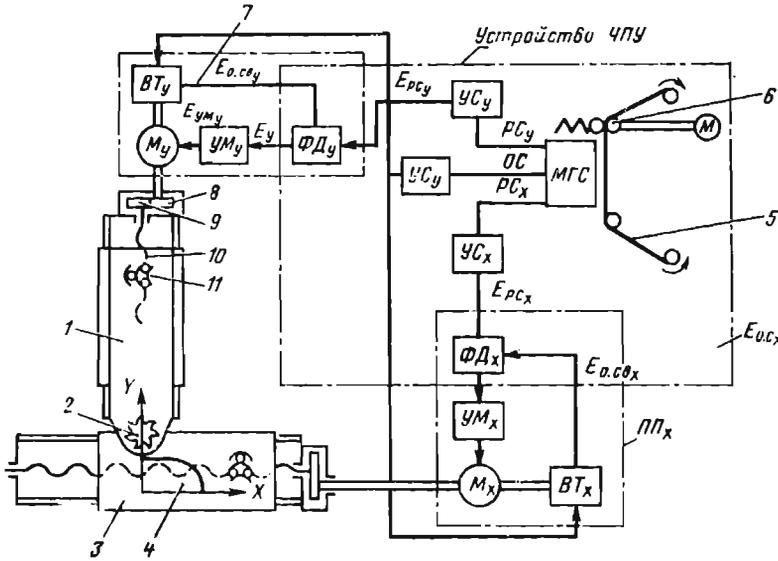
Схема фазовой системы ЧПУ фрезерного станка
